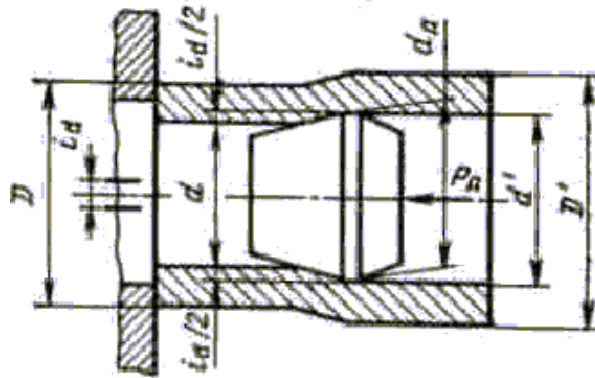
Розміри заготовки при об'ємному дорнуванні.
